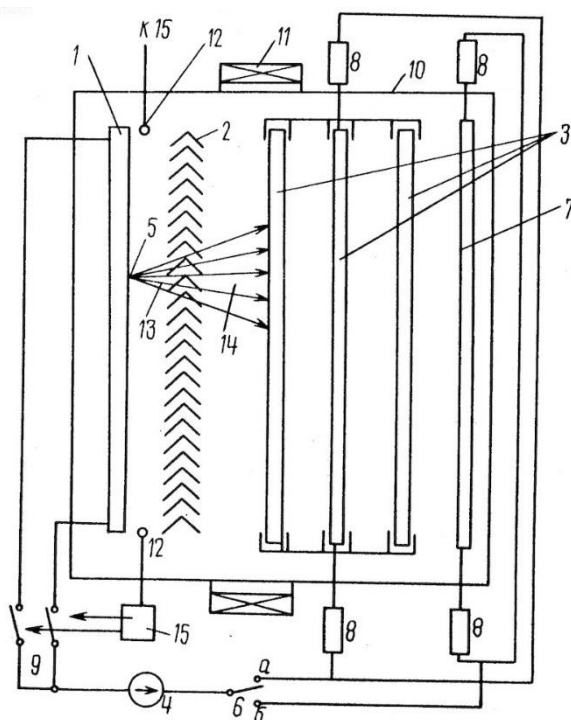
Схема установки по обработки изделий в плазме двухступенчатого вакуумно-дугового разряда. 1 – линейный катод; 2 – оптически непрозрачное приспособление(шеврон); 3 – обрабатываемые детали; 4 – источник питания дугового разряда; 5 – катодное пятно; 6 – двухпозиционный ключ; 7 – анод дугового разряда; 8 – выравнивающие резисторы; 9 – ключи токоподвода к катоду; 10 – вакуумная камера; 11 – соленоид; 12 – датчики крайнего расположения катодного пятна; 13 – столб газометаллической плазмы; 14 – столб газовой плазмы; 15 – блок управления перемещения катодного пятна.
